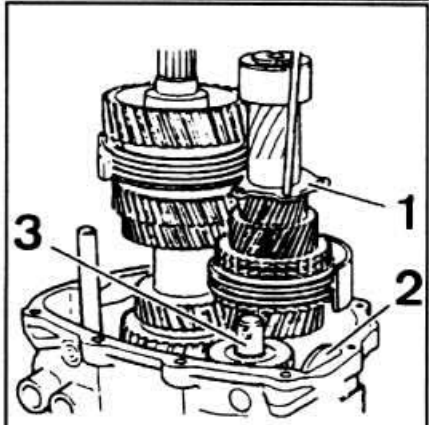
Положение деталей перед соединением задней крышки с картером КП:
